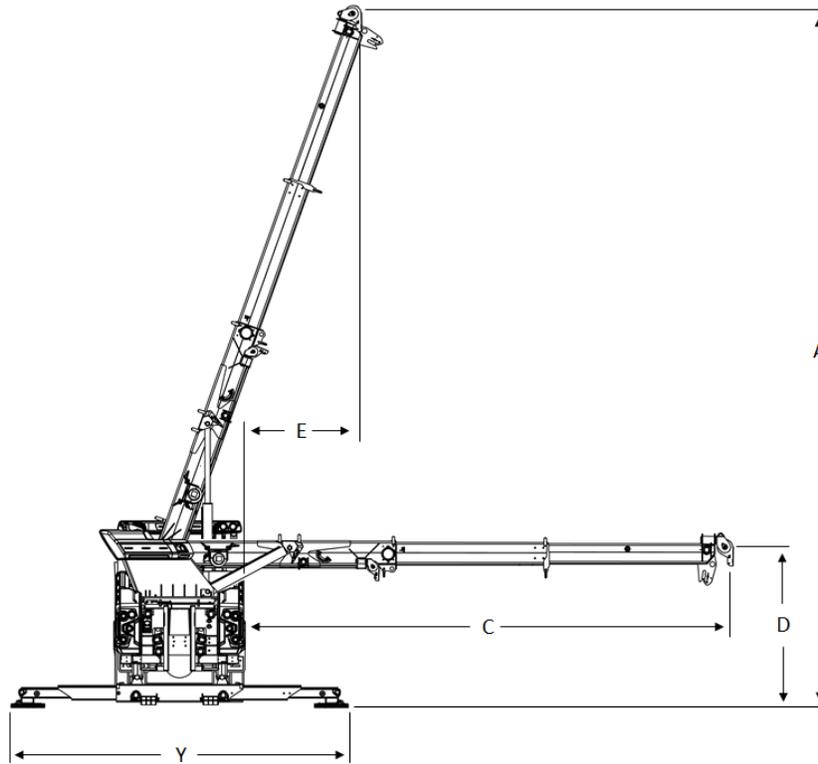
DIMENSIONS DE LA FLÈCHE ET DES STABILISATEURS - VUE ARRIÈRE (EXEMPLE)
